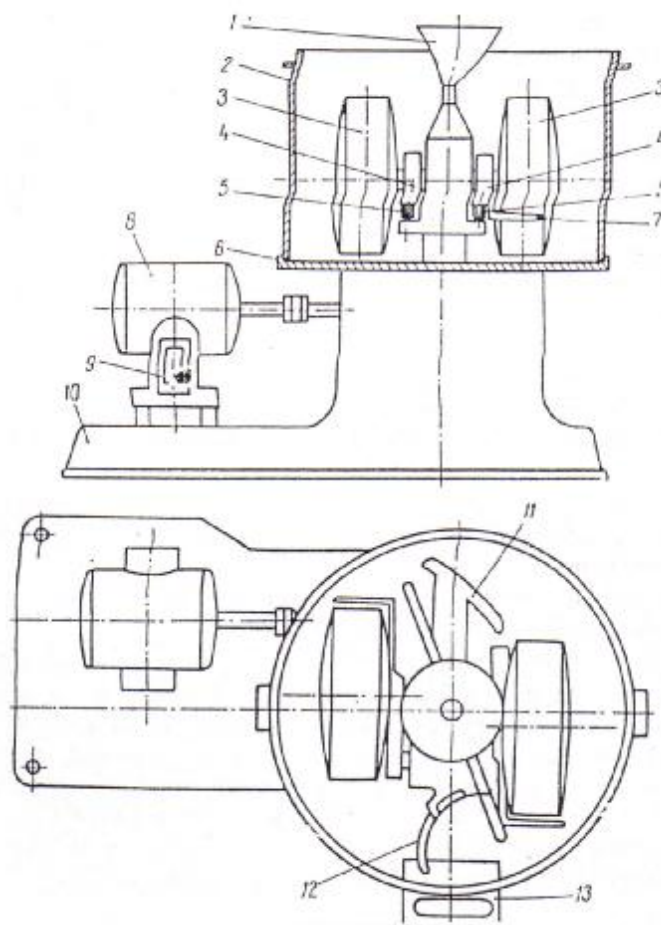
Malaxor de laborator : 1-pâlnie; 2-cuvă; 3-role de sfărâmare ; 4-lagăr mobil ; 5-șurub pentru reglarea distanței ; 6-placă de bază ; 7-răzuitor ; 8-electromotor ; 9-întrerupător ; 10-batiu ; 11 și 12- palete de dirijare ; 13-clapetă de evacuare.
